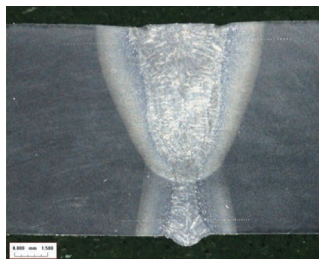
Сварное соединение, выполненное за два прохода с двух сторон [5]
